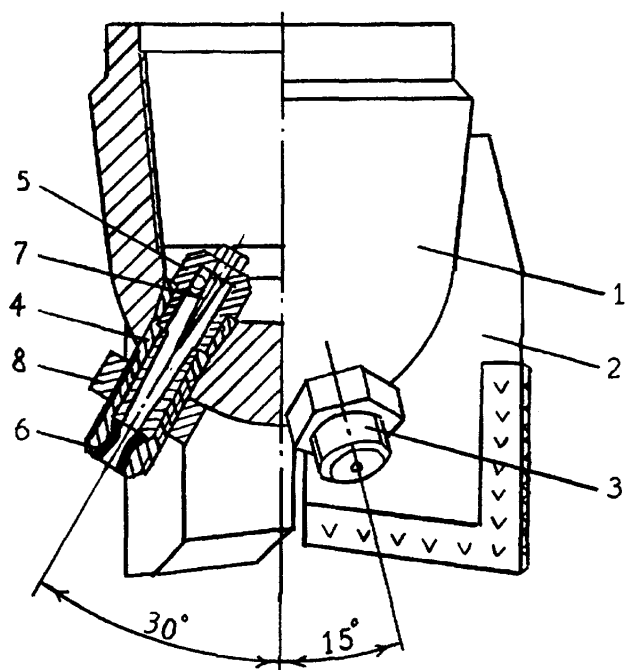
Трилопатеве бурове долото 3Л-295,3-ГП, вигляд з боку з половинним розрізом: 1 - корпус долота; 2 - лопаті долота; 3 - гідродинамічний пульсатор; 4 - корпус гідродинамічного пристрою; 5 - головка камери завихрення; 6 - насадка; 7 - шпиль-відбивач; 8 - гайка
